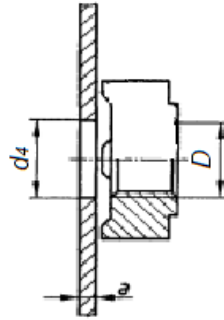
Присоединительные размеры (гайки еще не приварены)
